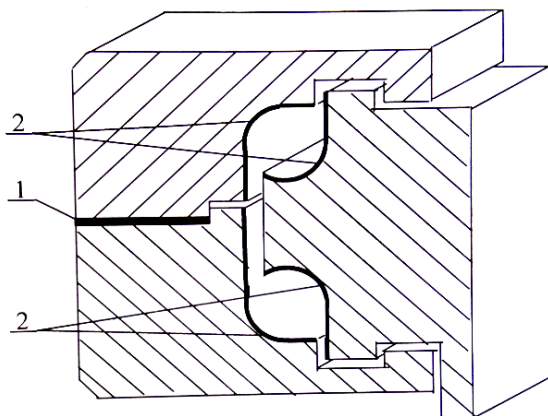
Поперечний переріз ОПК із зазначенням місць механічної обробки деталей: 1– роз'єм кілець; 2 – доріжки кочення; — місце механічної обробки [2]
